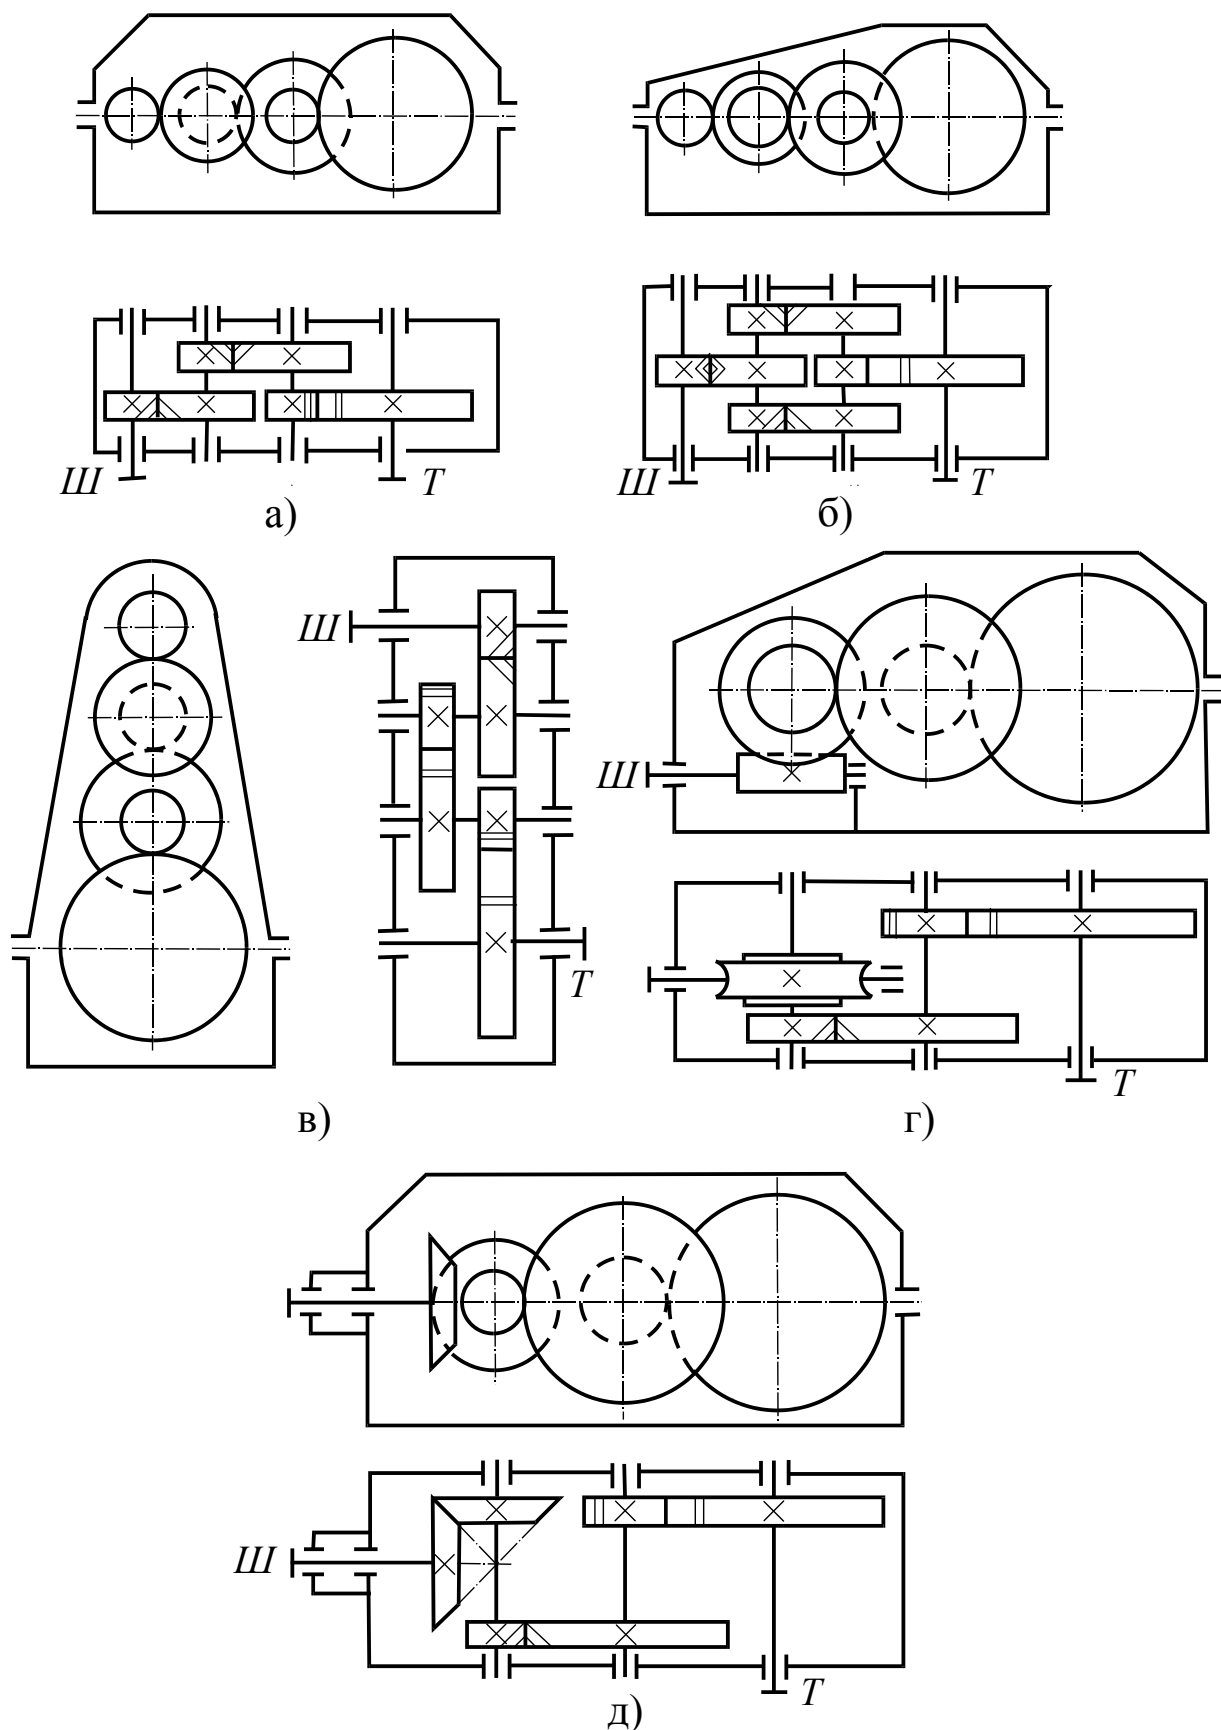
Кинематические схемы трехступенчатых редукторов: а) раз-
